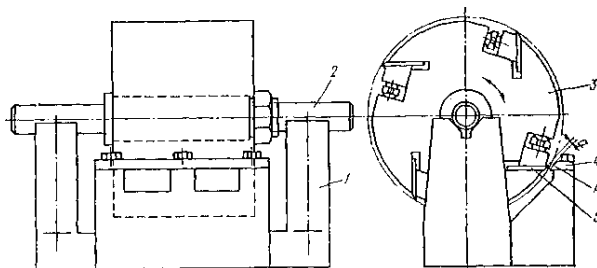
Пристосування для установки ножів у ножову головку чотирибічного поздовжньо-фрезерного верстата: 1 — основа; 2 — оправлення, 3 — ножова головка, 4 — планка, 5 — ніж
